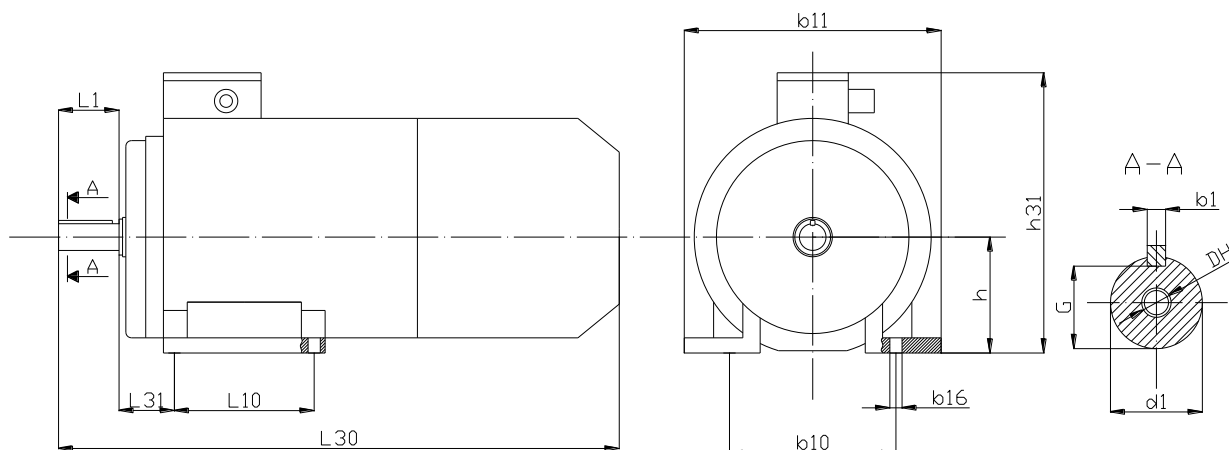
Габаритные и установочно-присоединительные размеры
